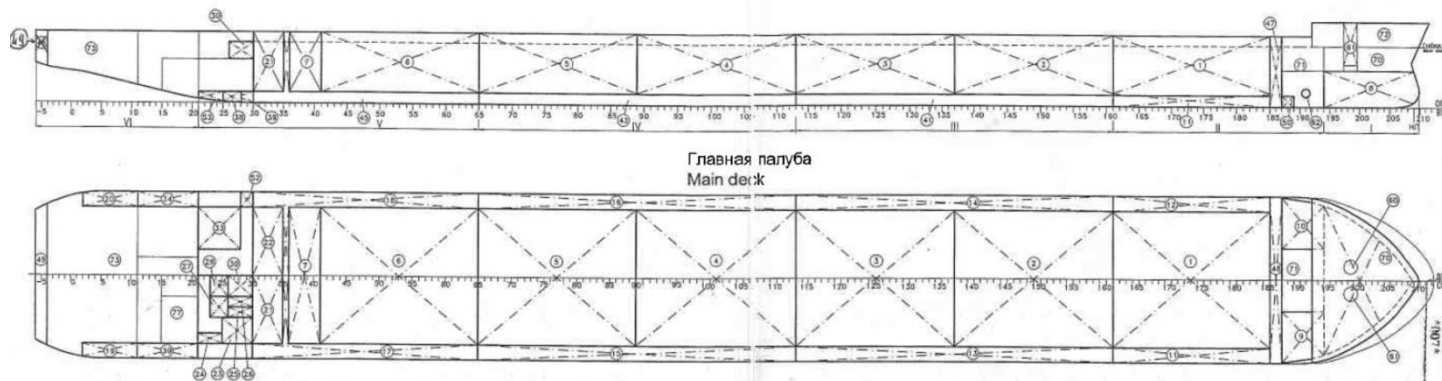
Схема расположения грузовых танков пр. 005-RST
